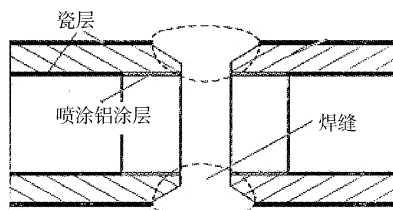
焊接接头内壁牺牲阳极防护法示意图
